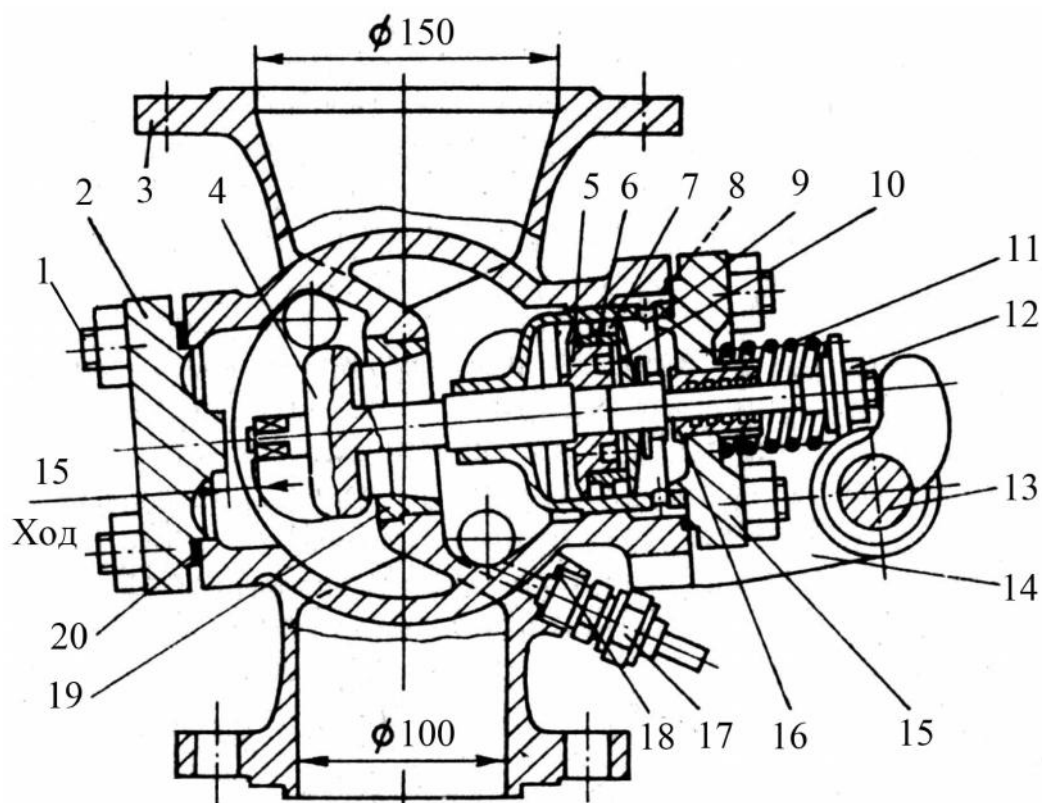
Главный предохранительный клапан: 1 – шпилька;
